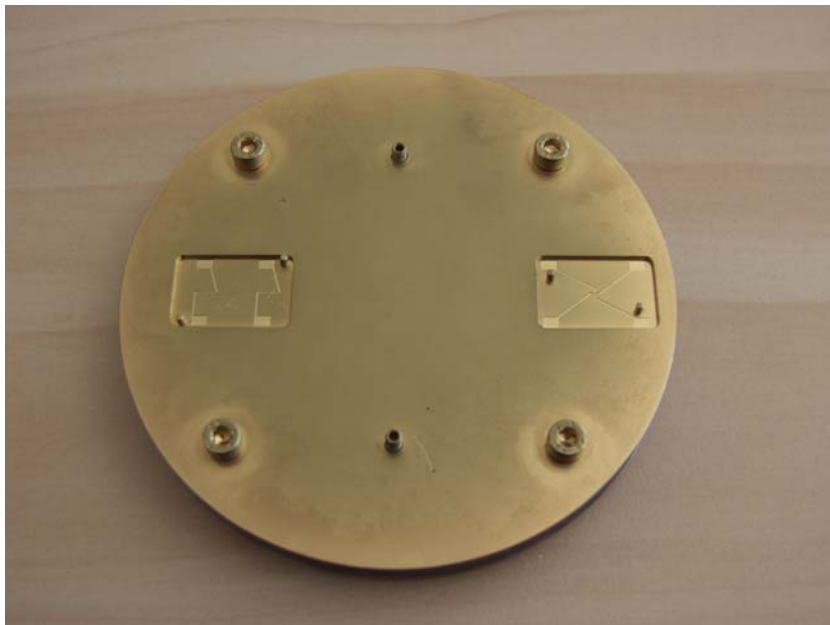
Maskenhalterung mit eingebautem CE-Chip
